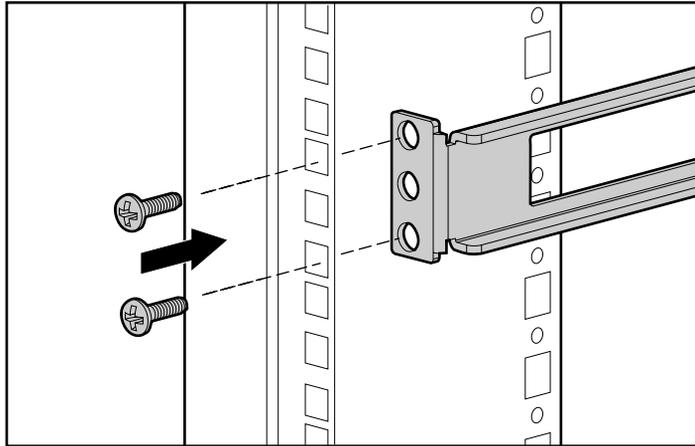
Installazione delle staffe di montaggio sulla parte anteriore del rack
